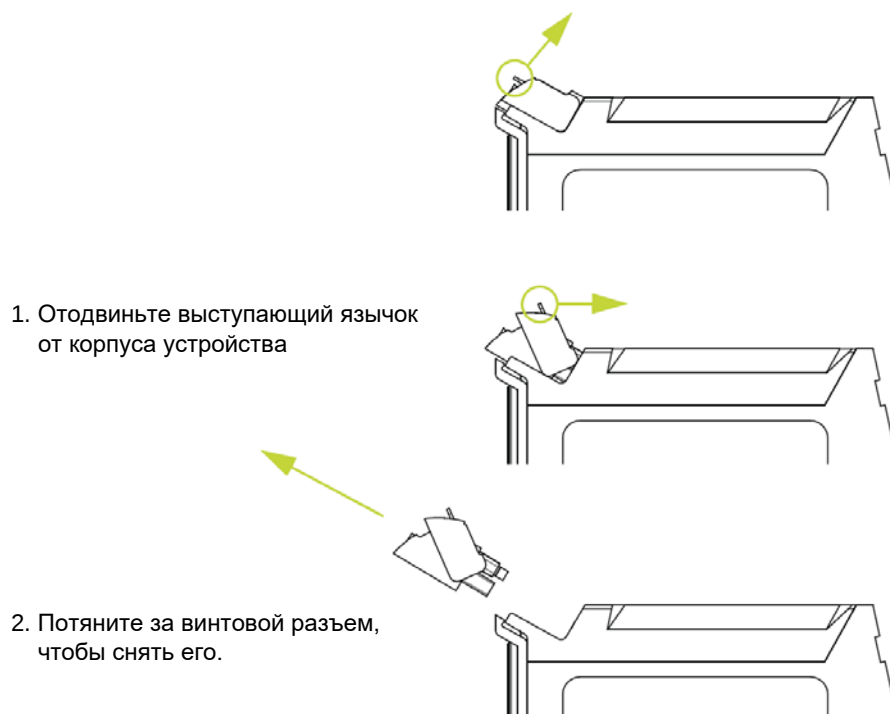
Удаление разъема с винтовыми зажимами из основного корпуса блока GSI127
